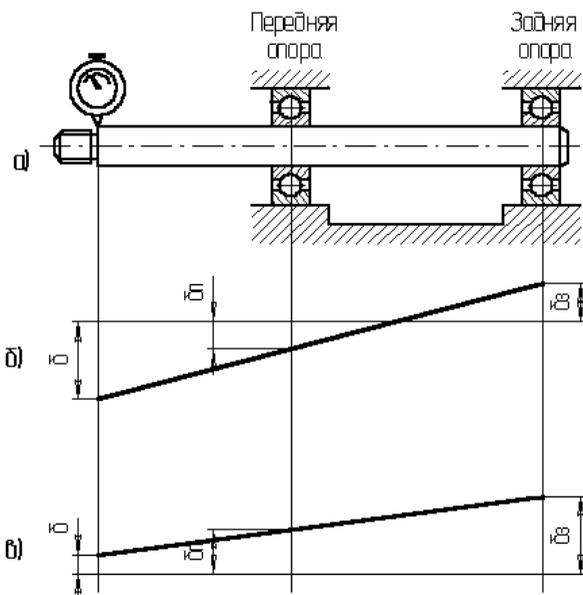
Схемы компенсации биения подшипников при монтаже вала
